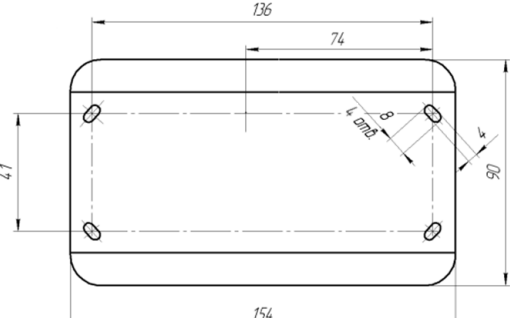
Розмітка отворів на основі корпусу оповіщувача
